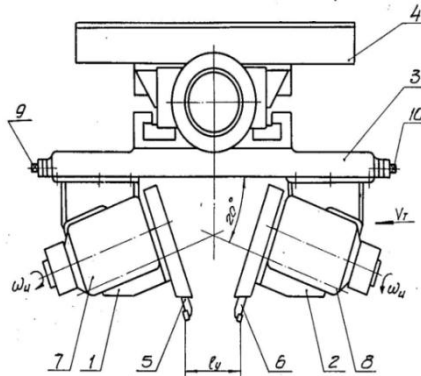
Принципиальная конструкция двухшпиндельного спецсуппорта к зубофрезерному станку мод. 5343
